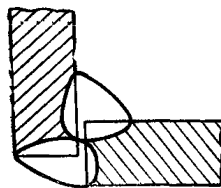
Сварное соединение угловое без скоса кромок двустороннее
